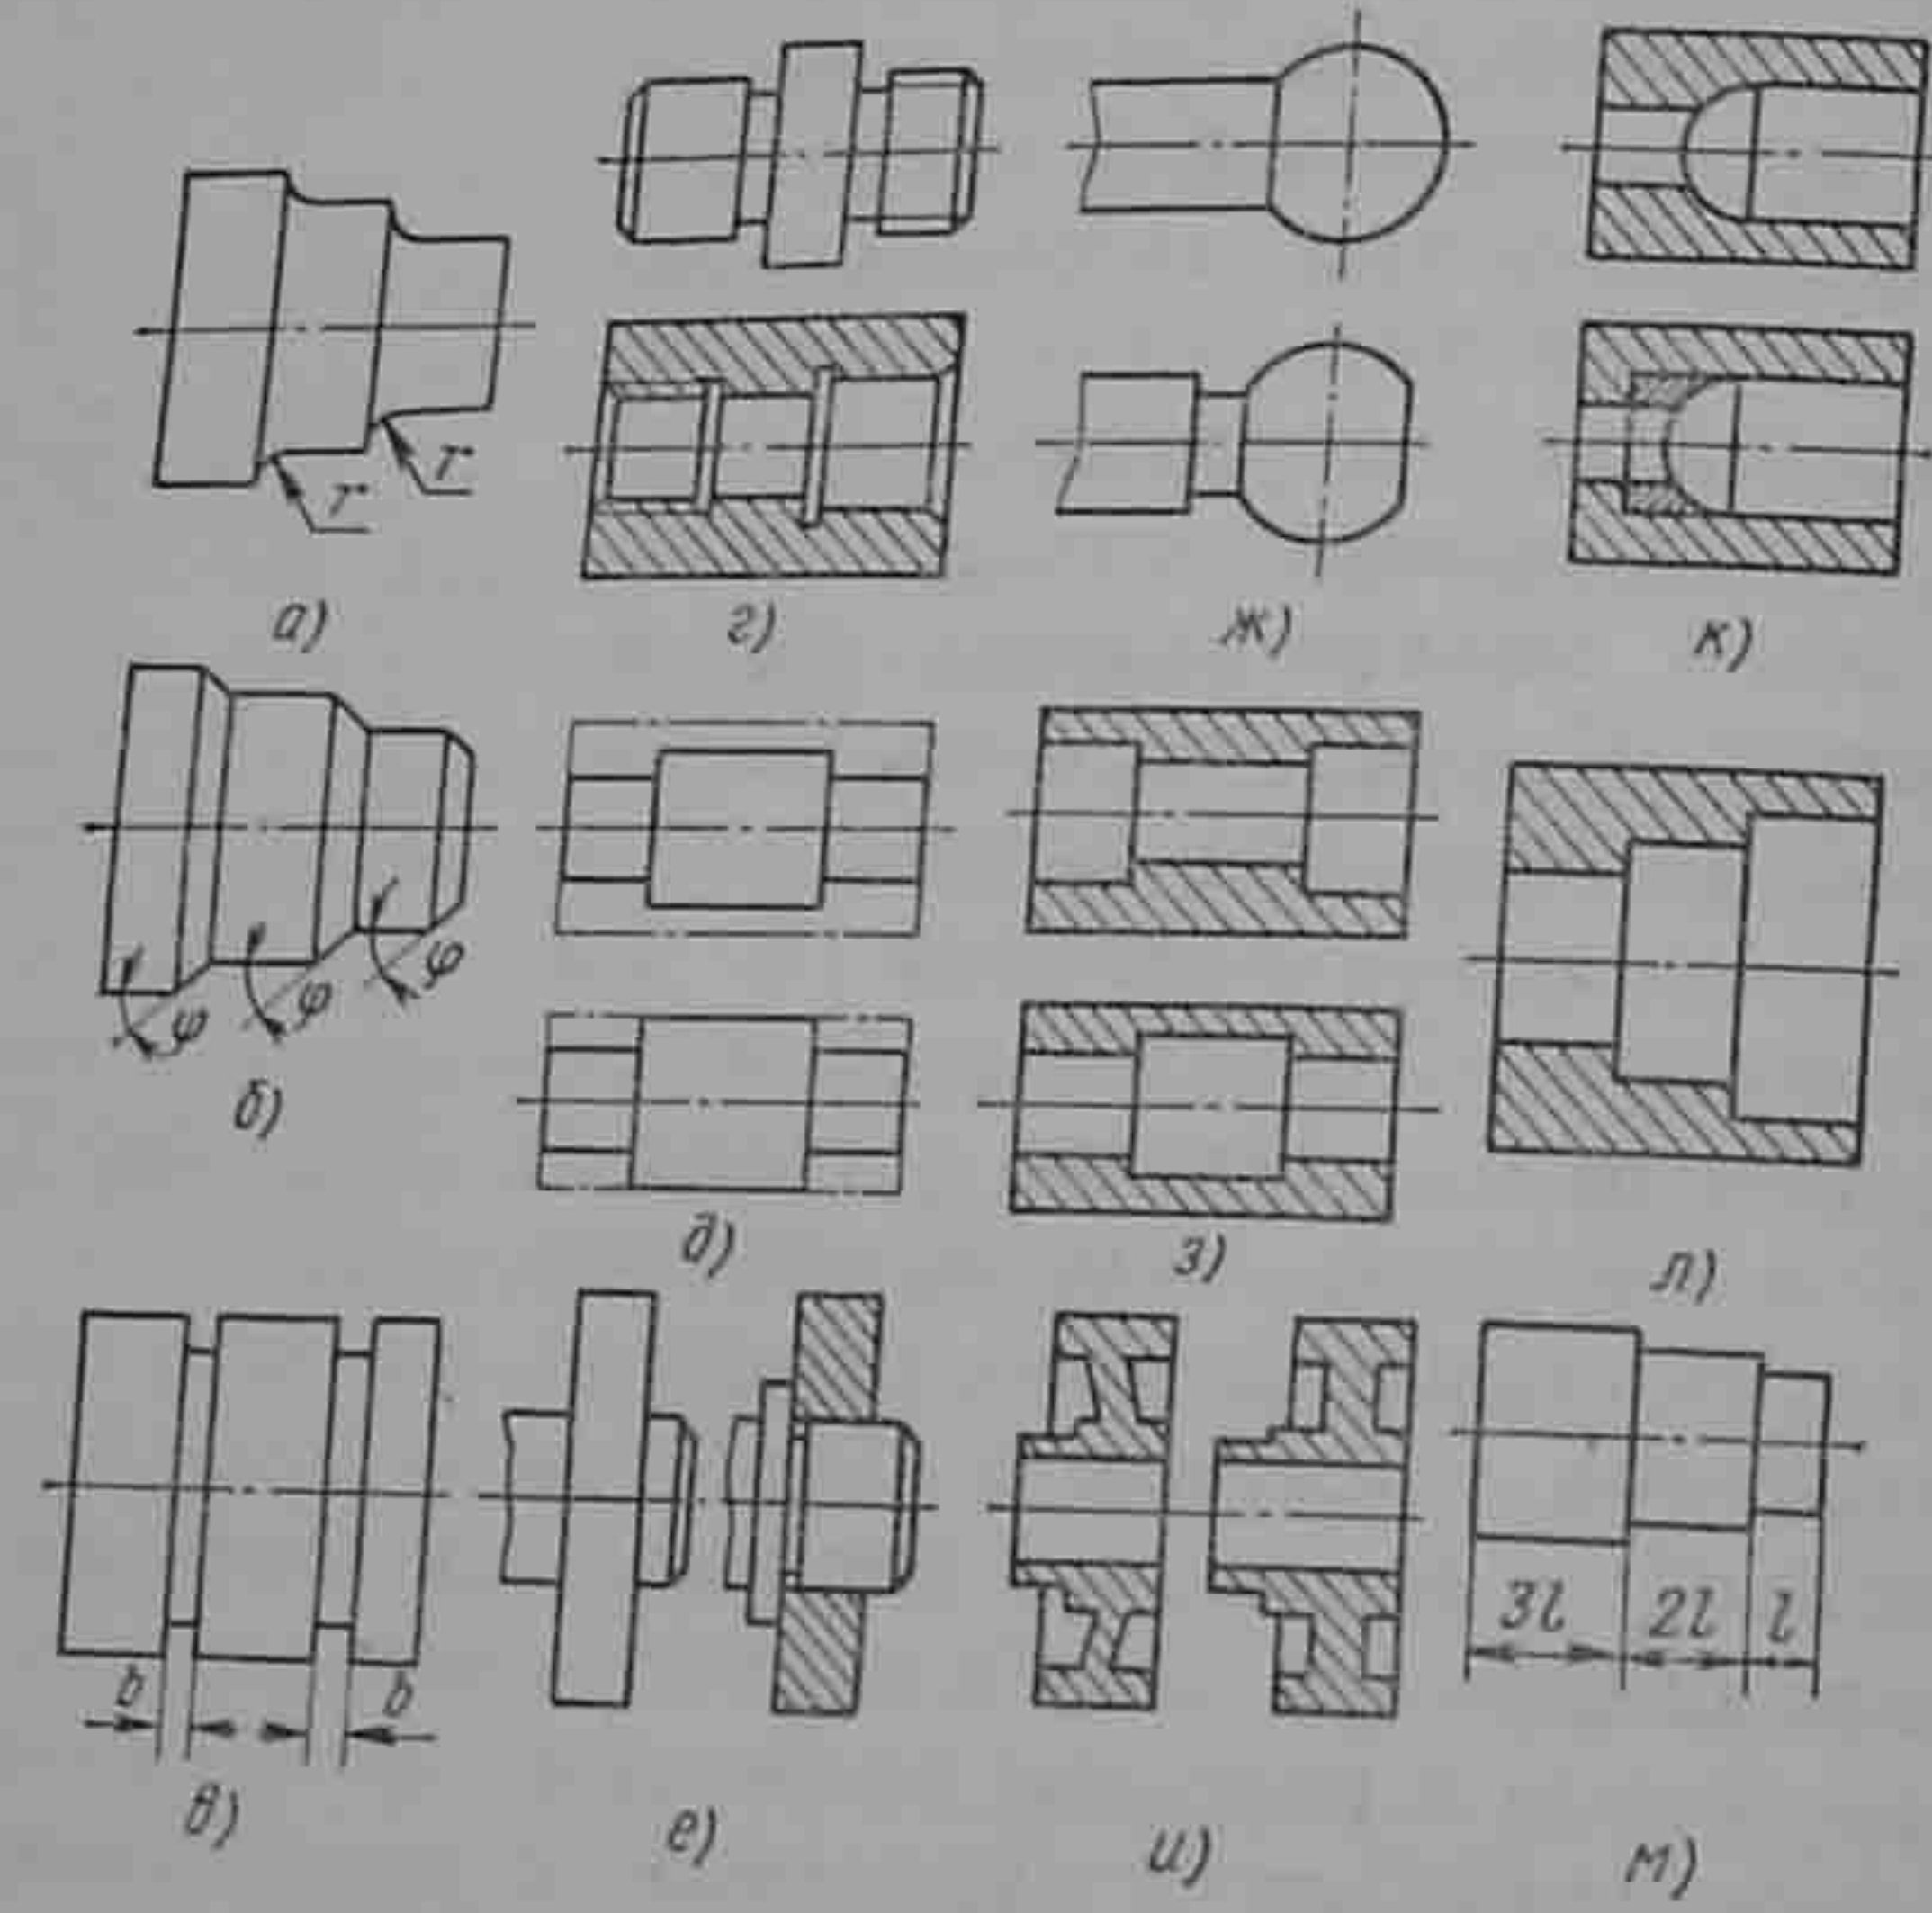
Примеры рациональных конструкций деталей машины, обрабатываемых на станках токарной группы
